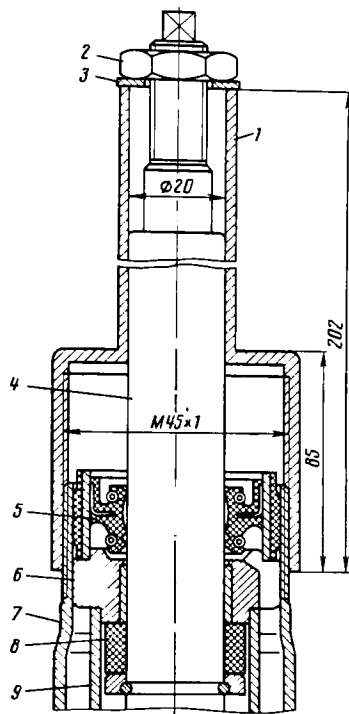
Съемник для выпрессовки манжеты штока амортизатора передней подвески:
